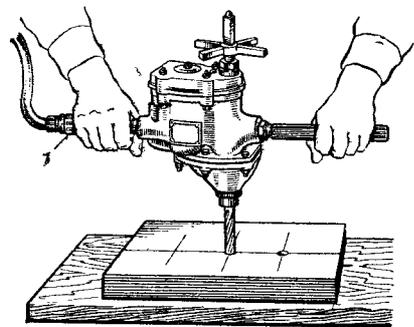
Прием вертикального сверления пневматической сверлильной машинкой
